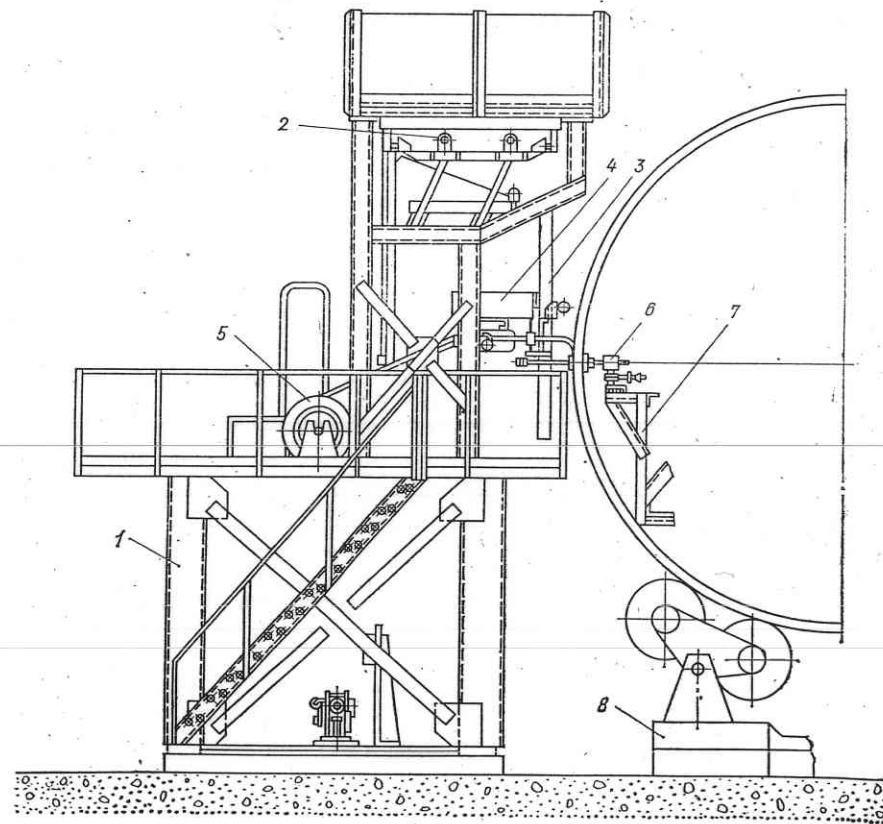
Установка для электрошлаковой сварки кольцевых поворотных стыков негабаритных трубопроводов:
